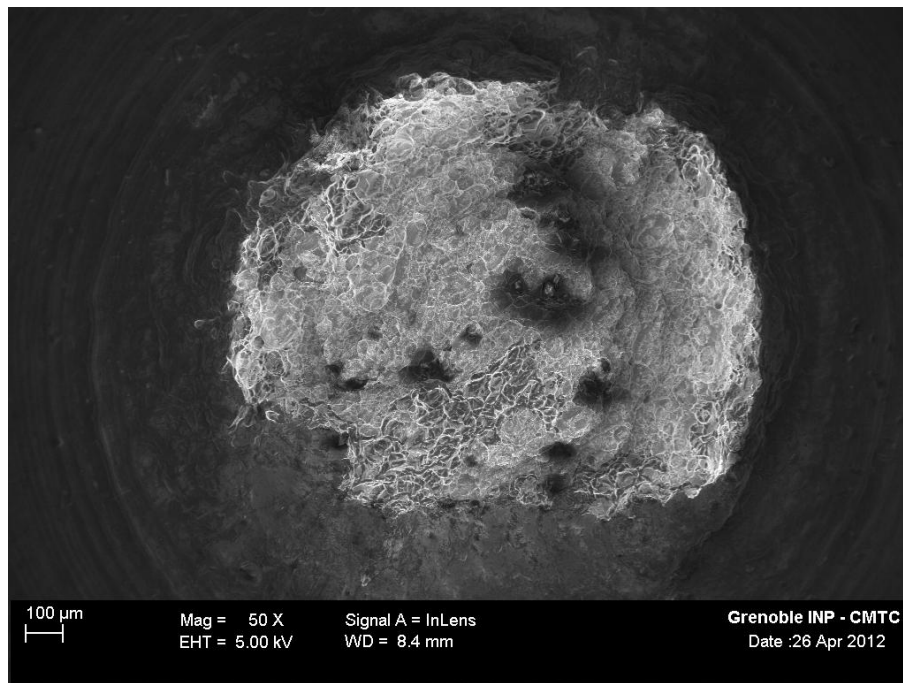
Fractografía de la probeta cilíndrica ASTM, con entalle en 90°, de cátodo. Se muestra la zona de fractura que se localiza en el entalle.
